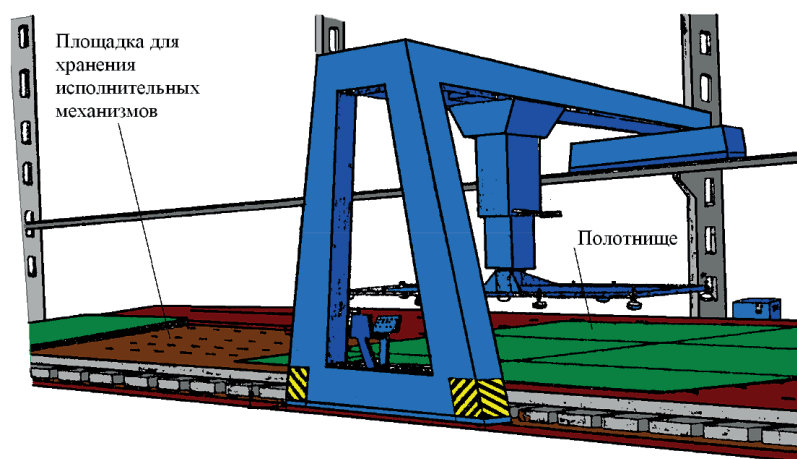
Общий вид многофункционального сборочно-сварочного манипулятора
